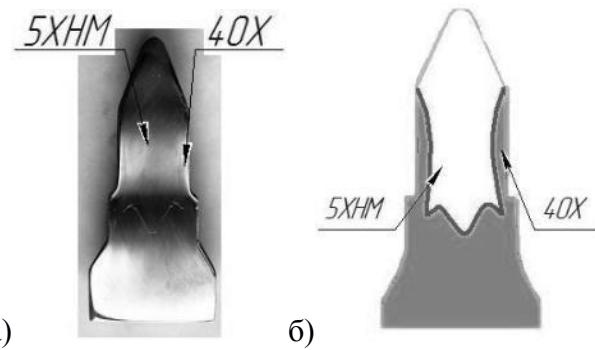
Вид биметаллического образца после деформации реальный образец (а) и модели (б)
